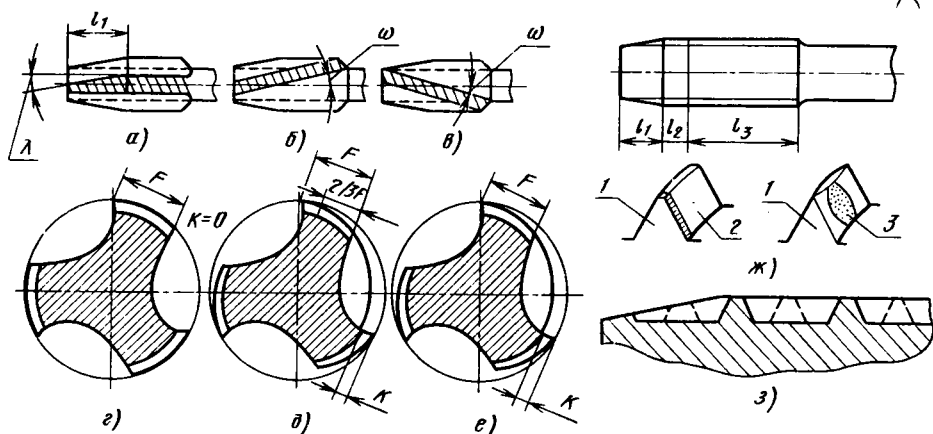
Конструктивное оформление режущей и калибрующей частей метчика
